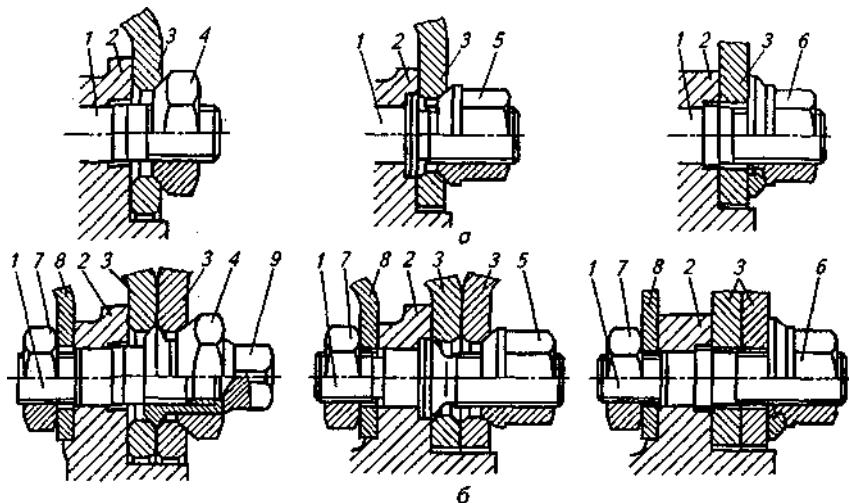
Крепление дисковых колес грузовых автомобилей: *a* — одинарных; *б* — сдвоенных; 1 — шпилька; 2 — ступица; 3 — диск; 4 — гайка крепления наружного диска; 5 — гайка типа ДИН; 6 — гайка с завалызованной шайбой; 7 — гайка крепления тормозного барабана; 8 — тормозной барабан; 9 — гайка крепления внутреннего диска
